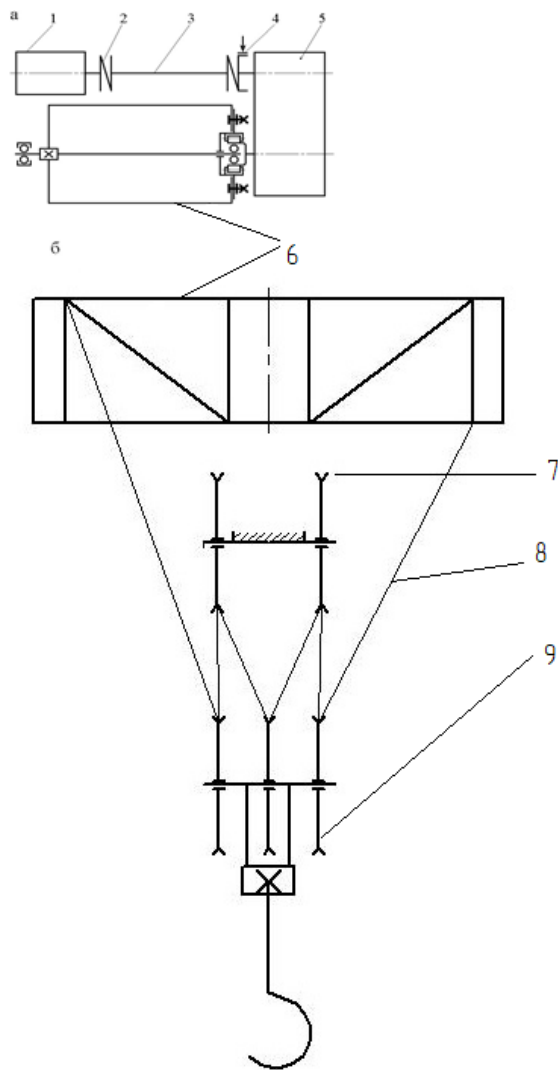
Кинематическая схема механизма подъема: а – лебедка; б – запасовка канатов;
